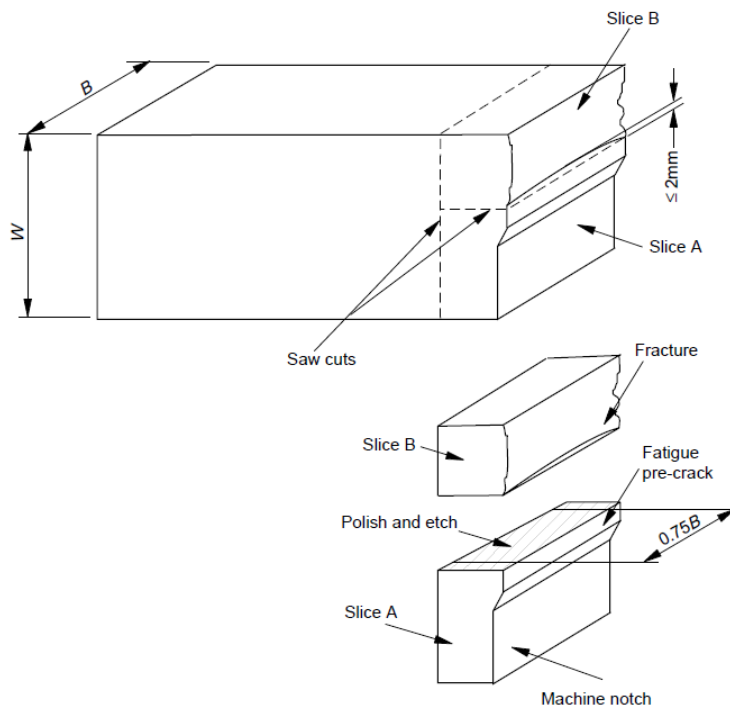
Cortes de las superficies de fractura para la observación del frente de grieta
